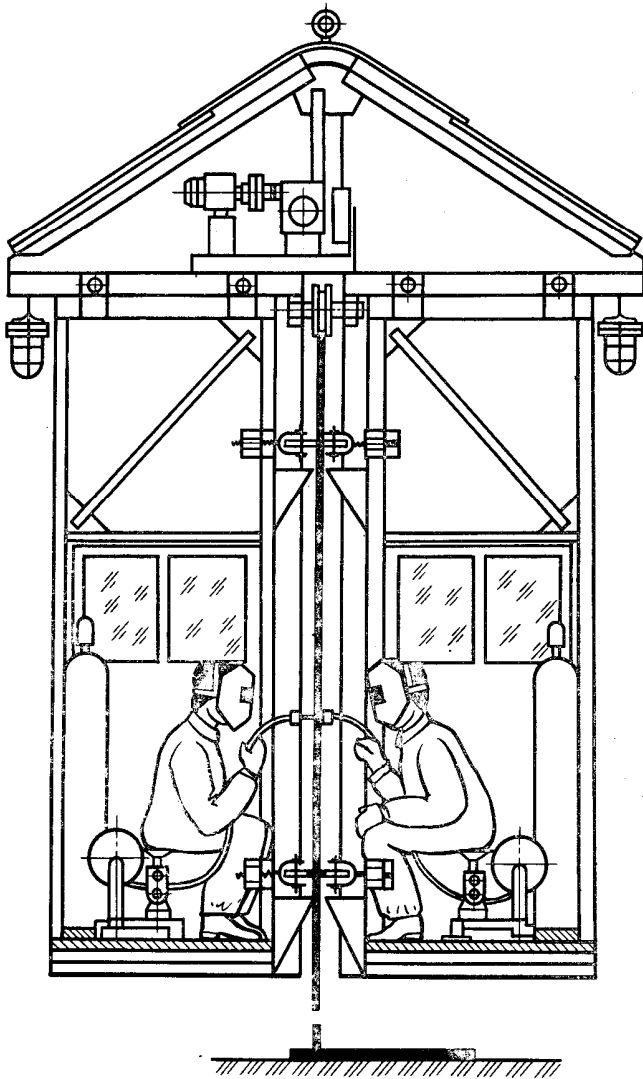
Сварка горизонтального шва полуавтоматами
